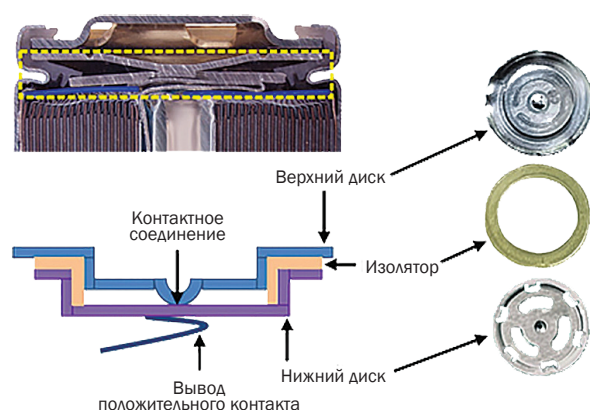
Общий вид и схема устройства прерывания тока «CID»
